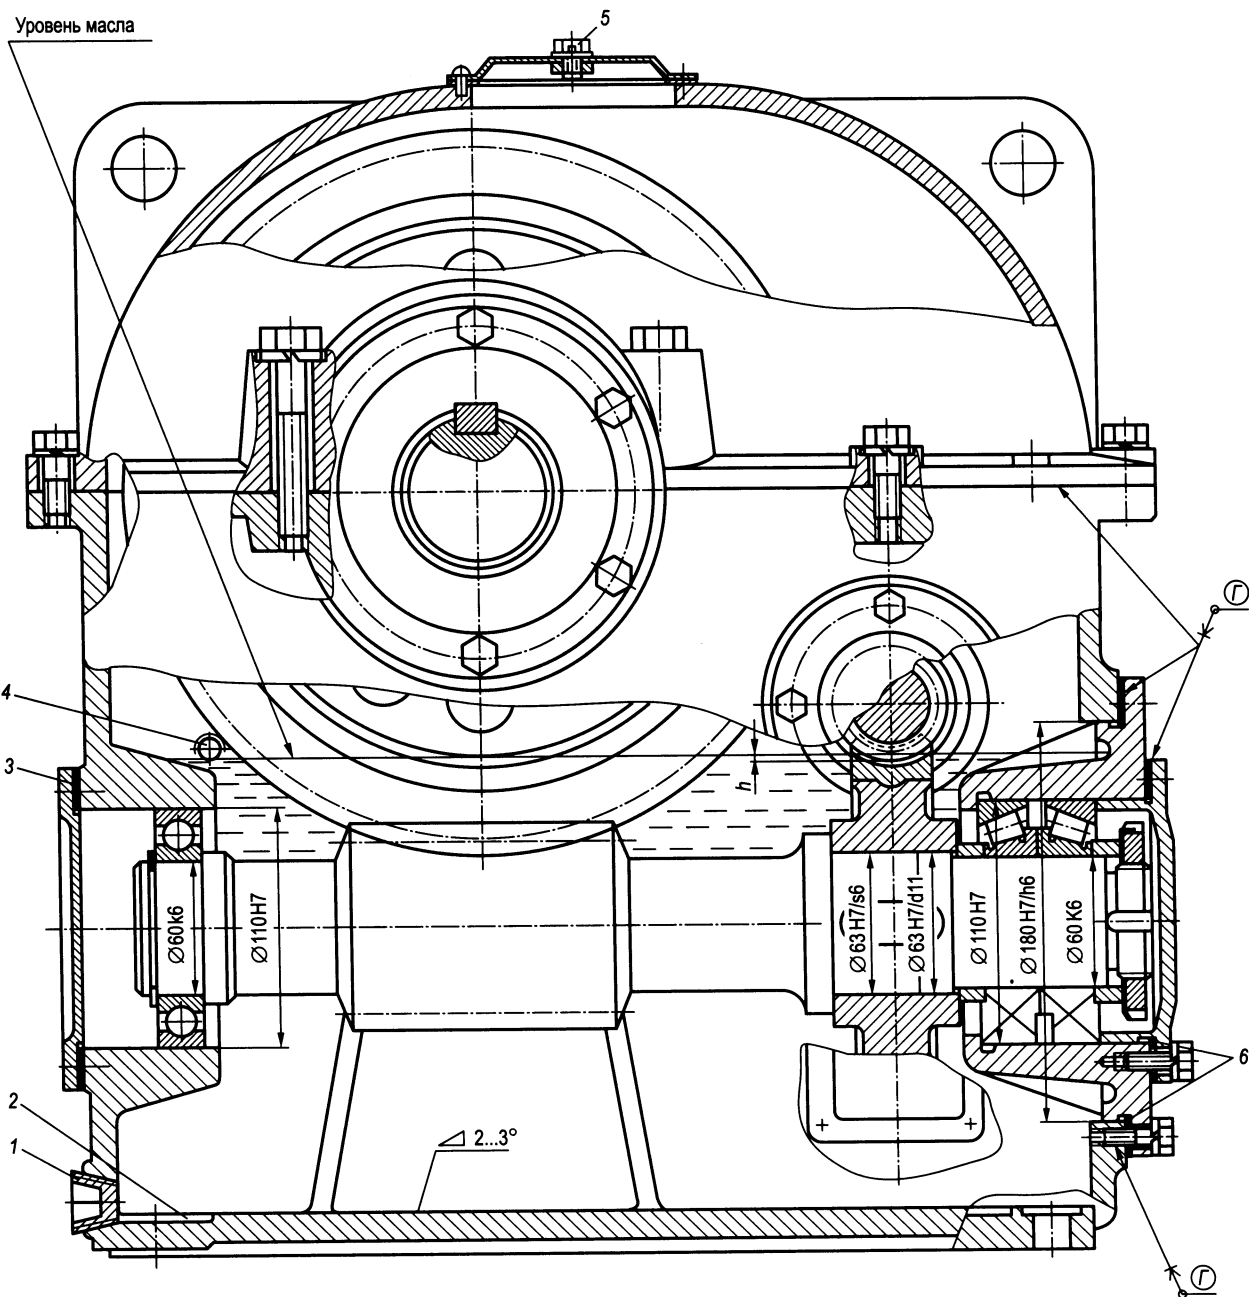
Двухступенчатый червячный редуктор с погружением быстроходного червяка в масляную ванну на глубину $h = (1...2) m$:
